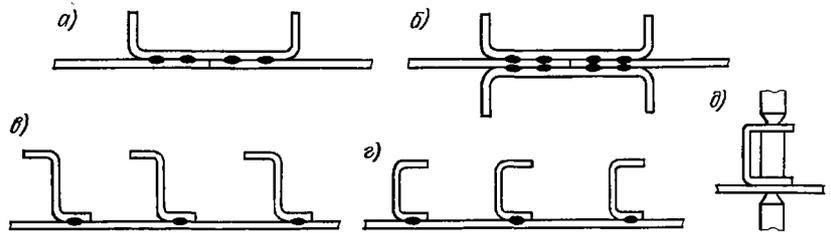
Виды крупногабаритных точечно-сварных конструкций
